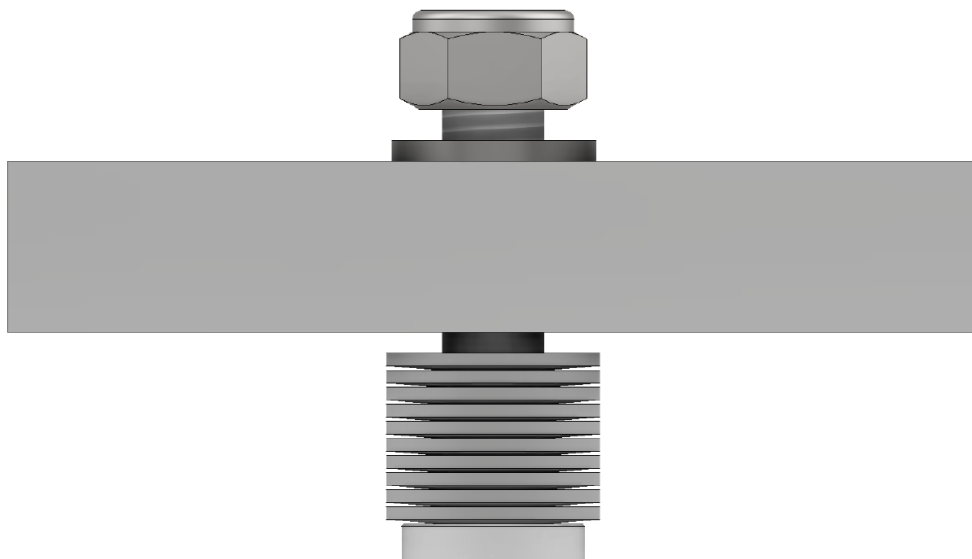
Fase “zero” di assemblaggio di un bar clamp
